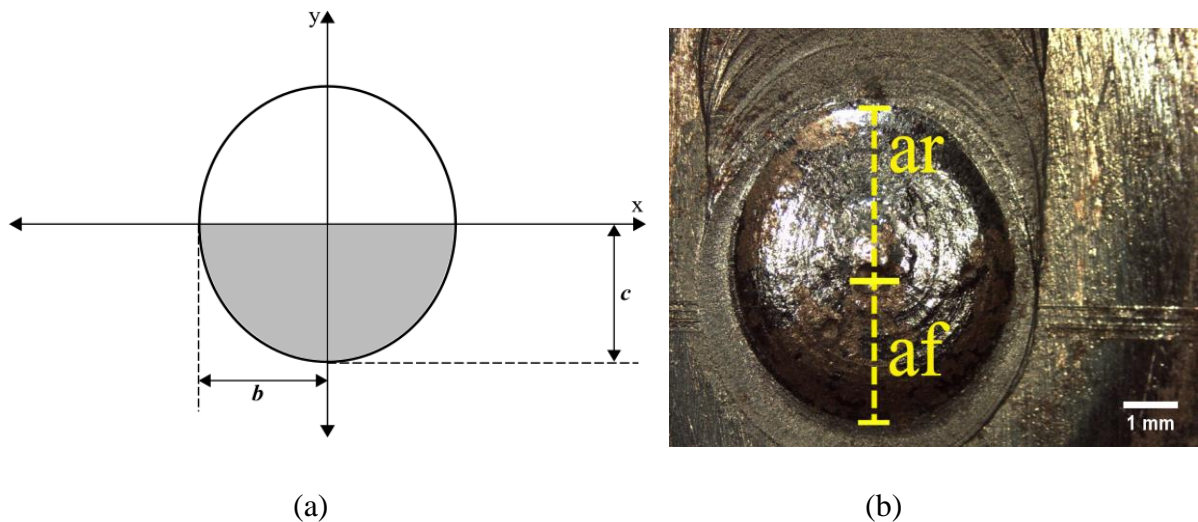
Esquema das dimensões da seção transversal de cordão de solda TIG (a); dimensões da poça de fusão TIG (b). Fonte: Autor.
